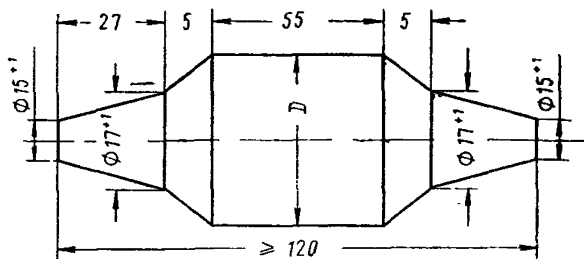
Форма и размеры поволоков для изготовления пары электродов с наружным конусом к машинам типа МТП-75 (100)
